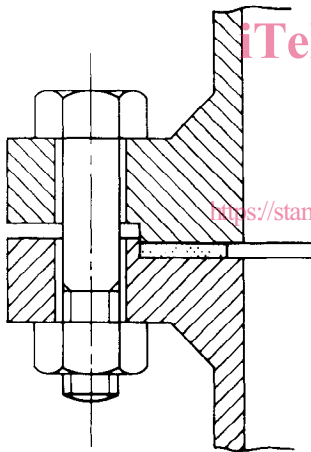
Face de joint de type E/F avec joint à emboîtement simple mâle/femelle
